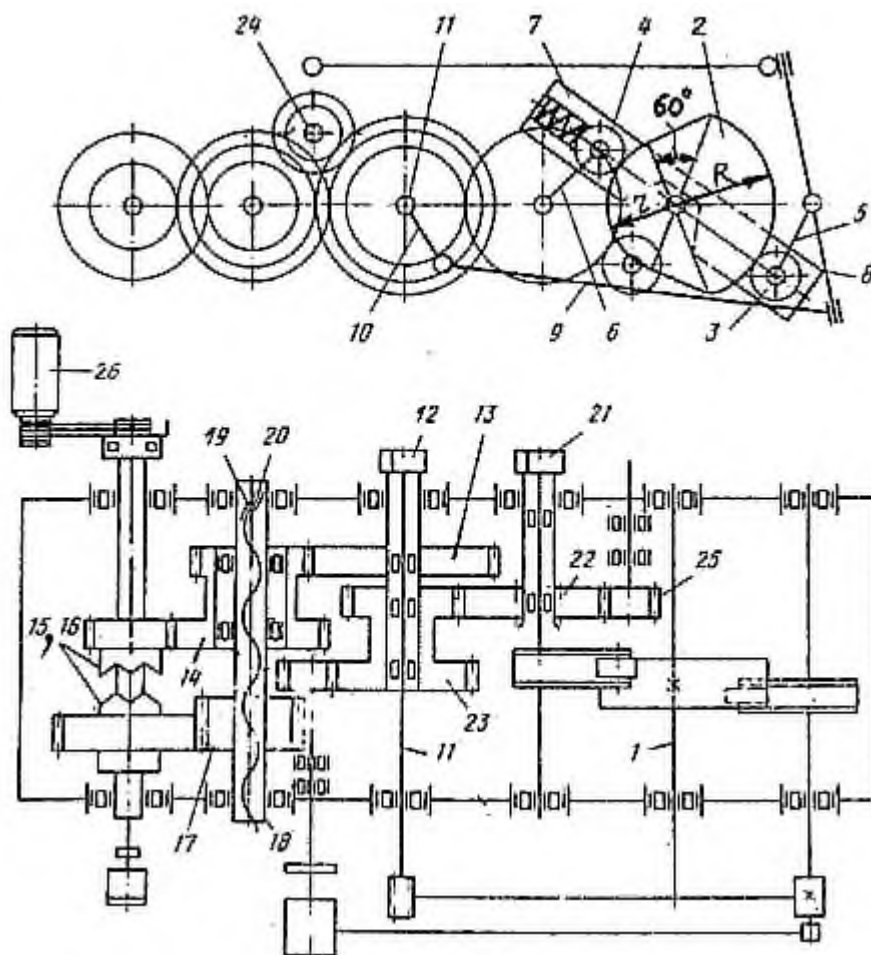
Кинематическая схема механизма подачи и поворота редукторного типа ХПТ [1]
